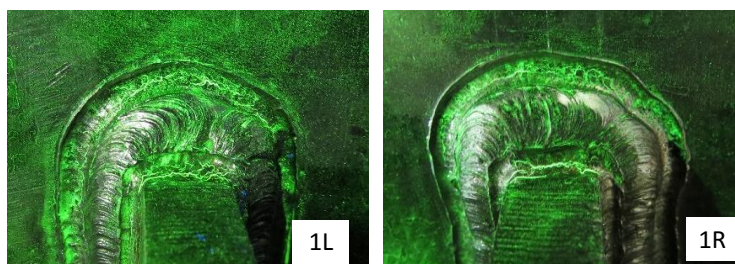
溶接のままの UIT を施工した試験体の磁粉探傷試験
